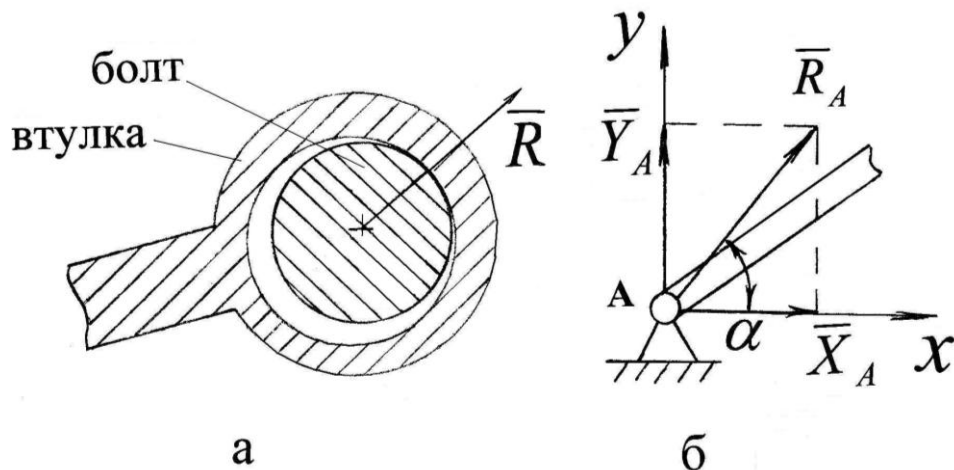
Неподвижный цилиндрический шарнир или подшипник
